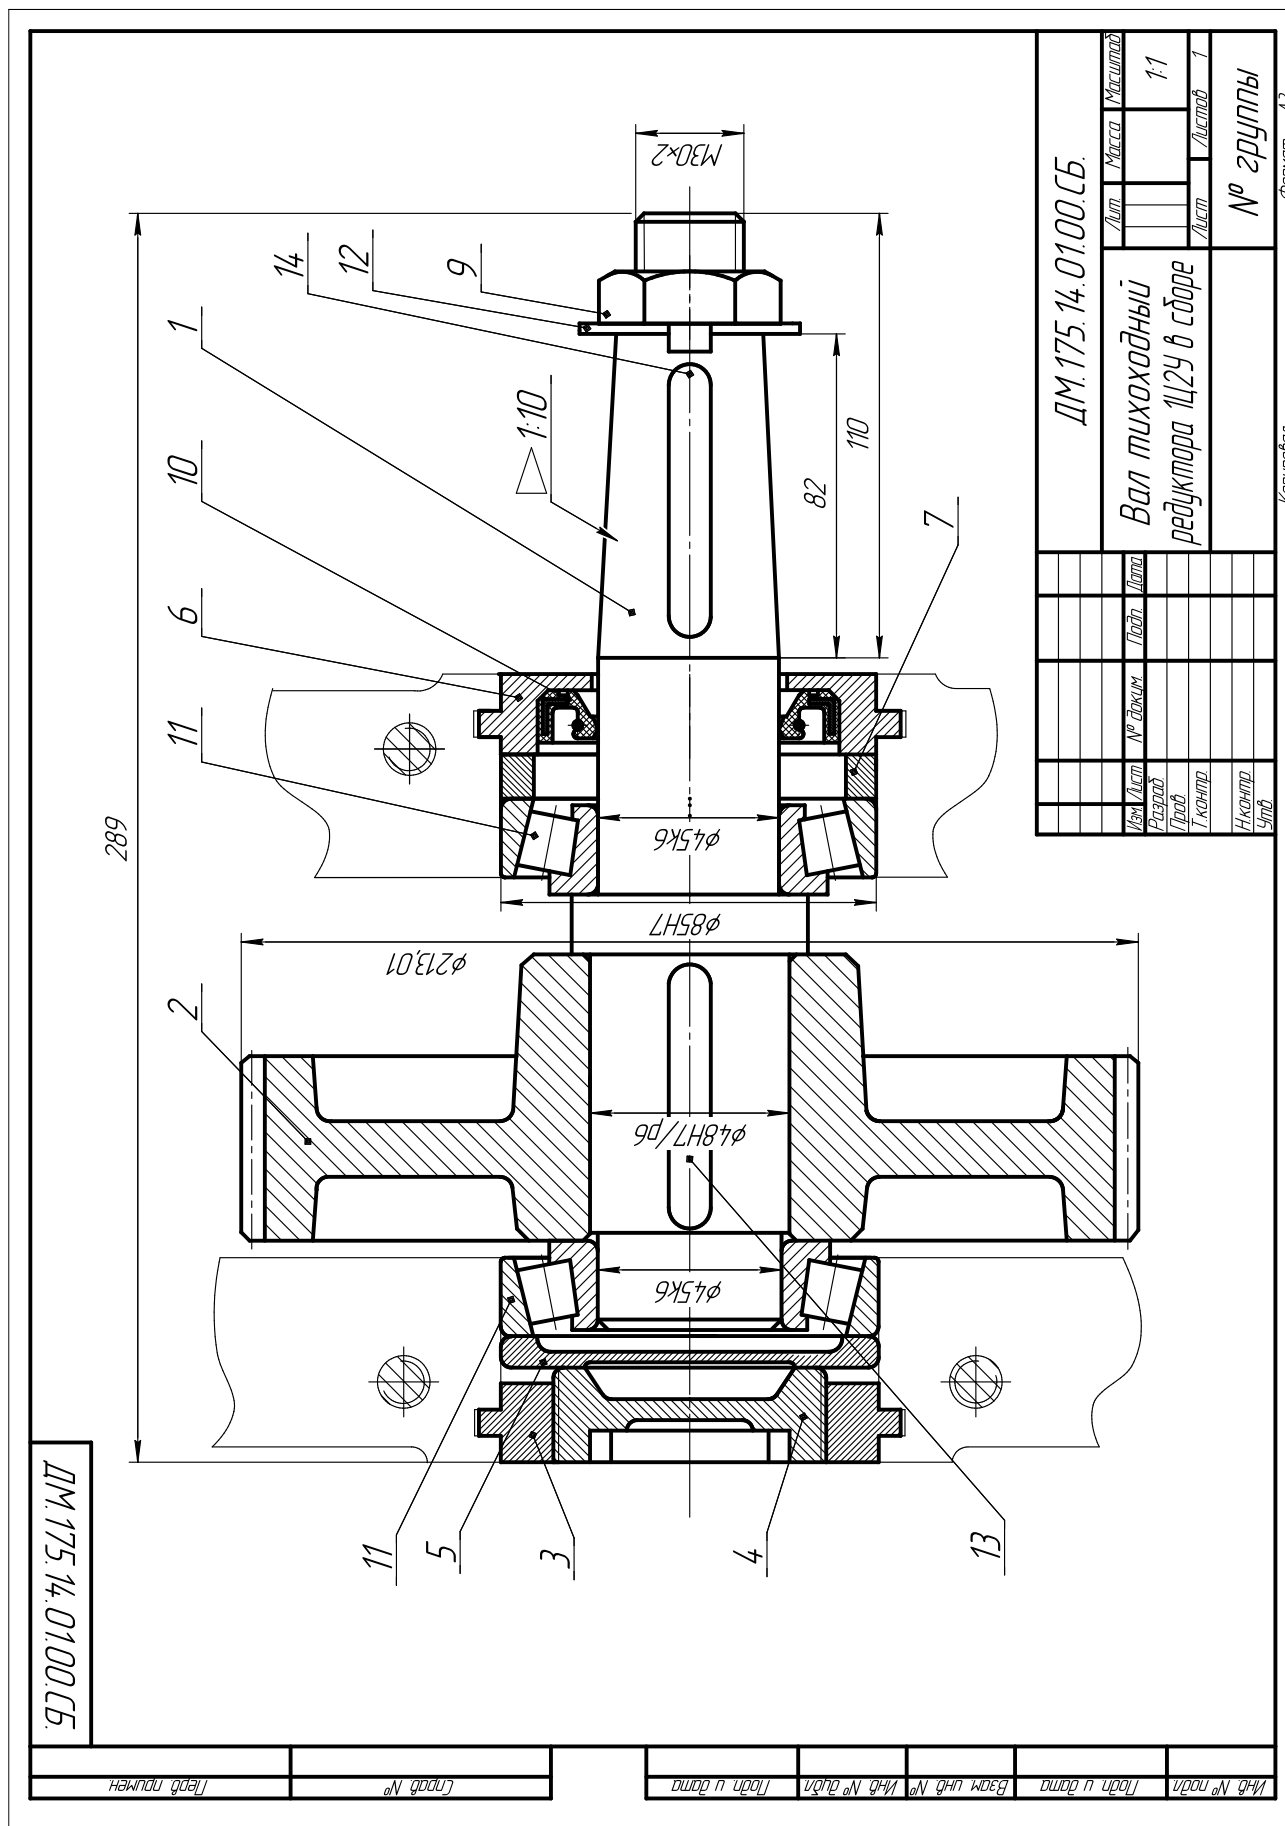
Пример оформления сборочного чертежа тихоходного вала редуктора 1Ц2У-125
